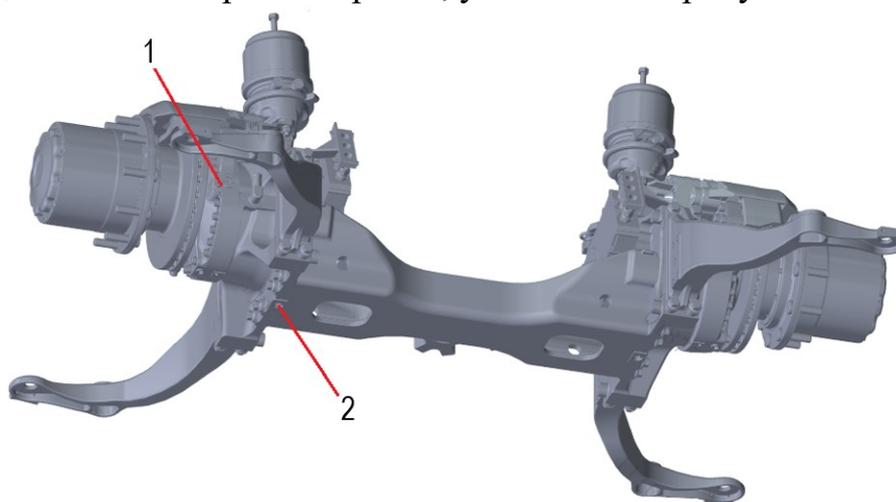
Расположение отверстий бортового редуктора:
